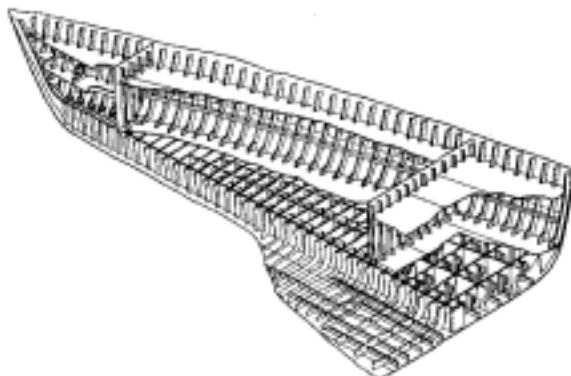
Несколько видов конструкций акваторийного транспортного судна
